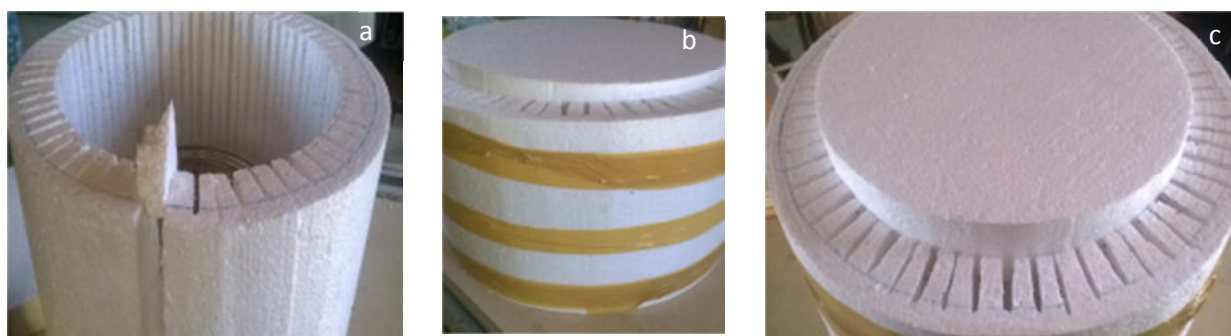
a), b) y c): cerrado de la plancha para formar el círculo, alistado de la tapa y secado sujetado con cinta adhesiva.
